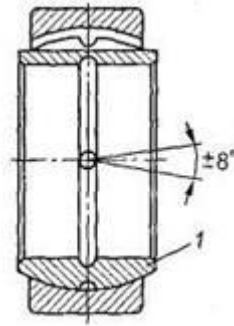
Самоустанавливающийся подшипник: 1 — вкладыш
